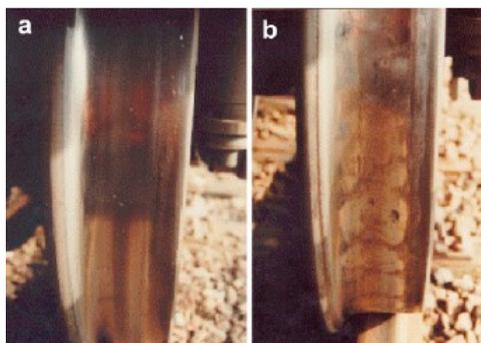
Superfície de rolamento de roda com (a) sistema de frenagem de discos, (b) sistema de frenagem de cepos atuantes na roda.
